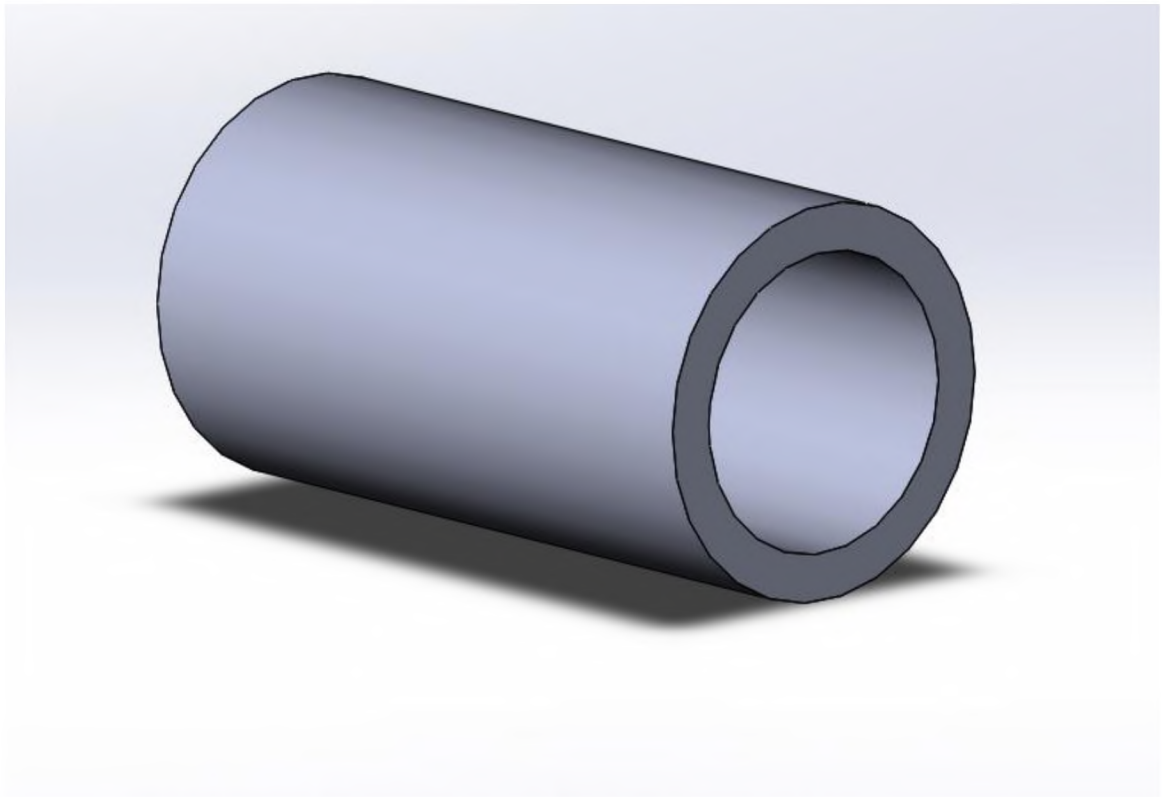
3D модель заготовки деталі «Втулка»
